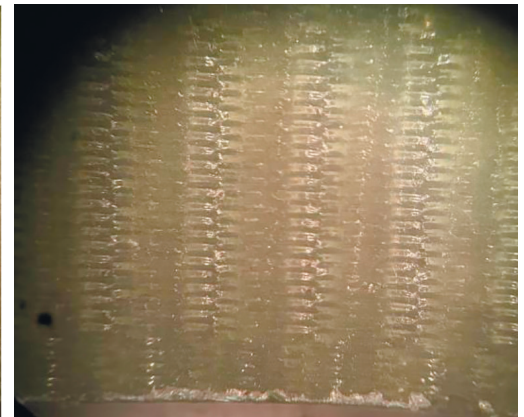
Наилучшая шероховатость при фрезеровании периферией фрезы
